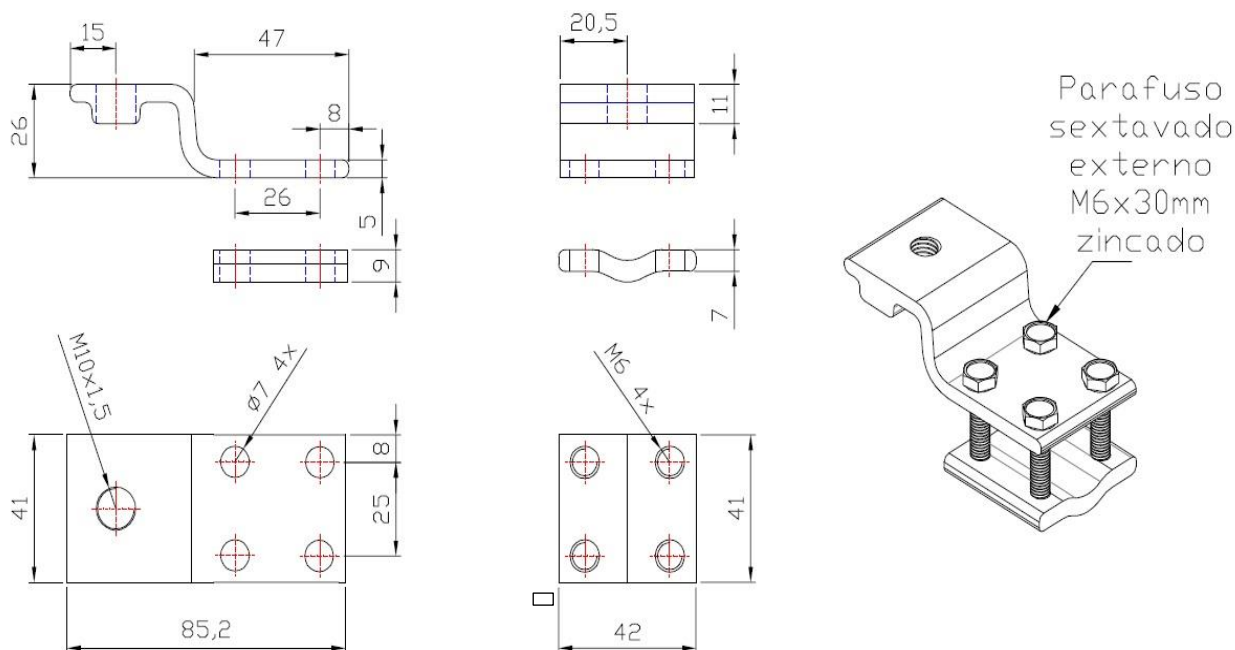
Terminal de aterramento “Z”, em alumínio, fabricado pelo processo de extrusão e estampagem.
